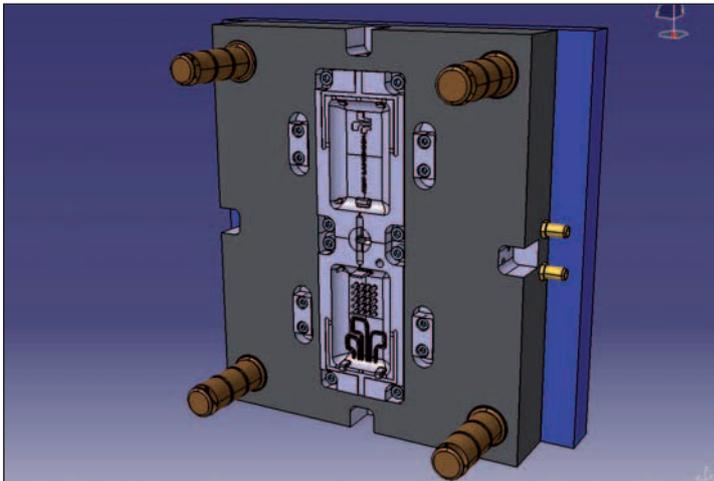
(2): 3D-Entwurf Kunststoffspritzgusswerkzeug (Düsenseite)
